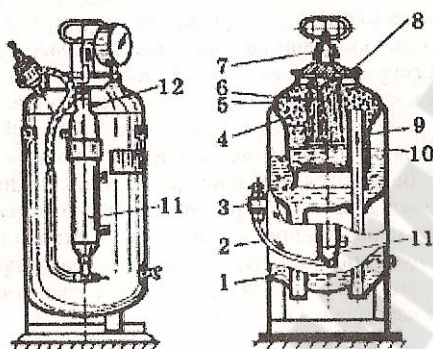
7. Схема ацетиленового генератора: 1 – промыватель; 2 – шланг; 3 – предохранительный клапан; 4 – газообразователь; 5 – шахта; 6 – корзина; 7 – винтовой зажим; 8 – крышка; 9 – стакан; 10 – труба; 11 – водяной затвор; 12 – ниппель
